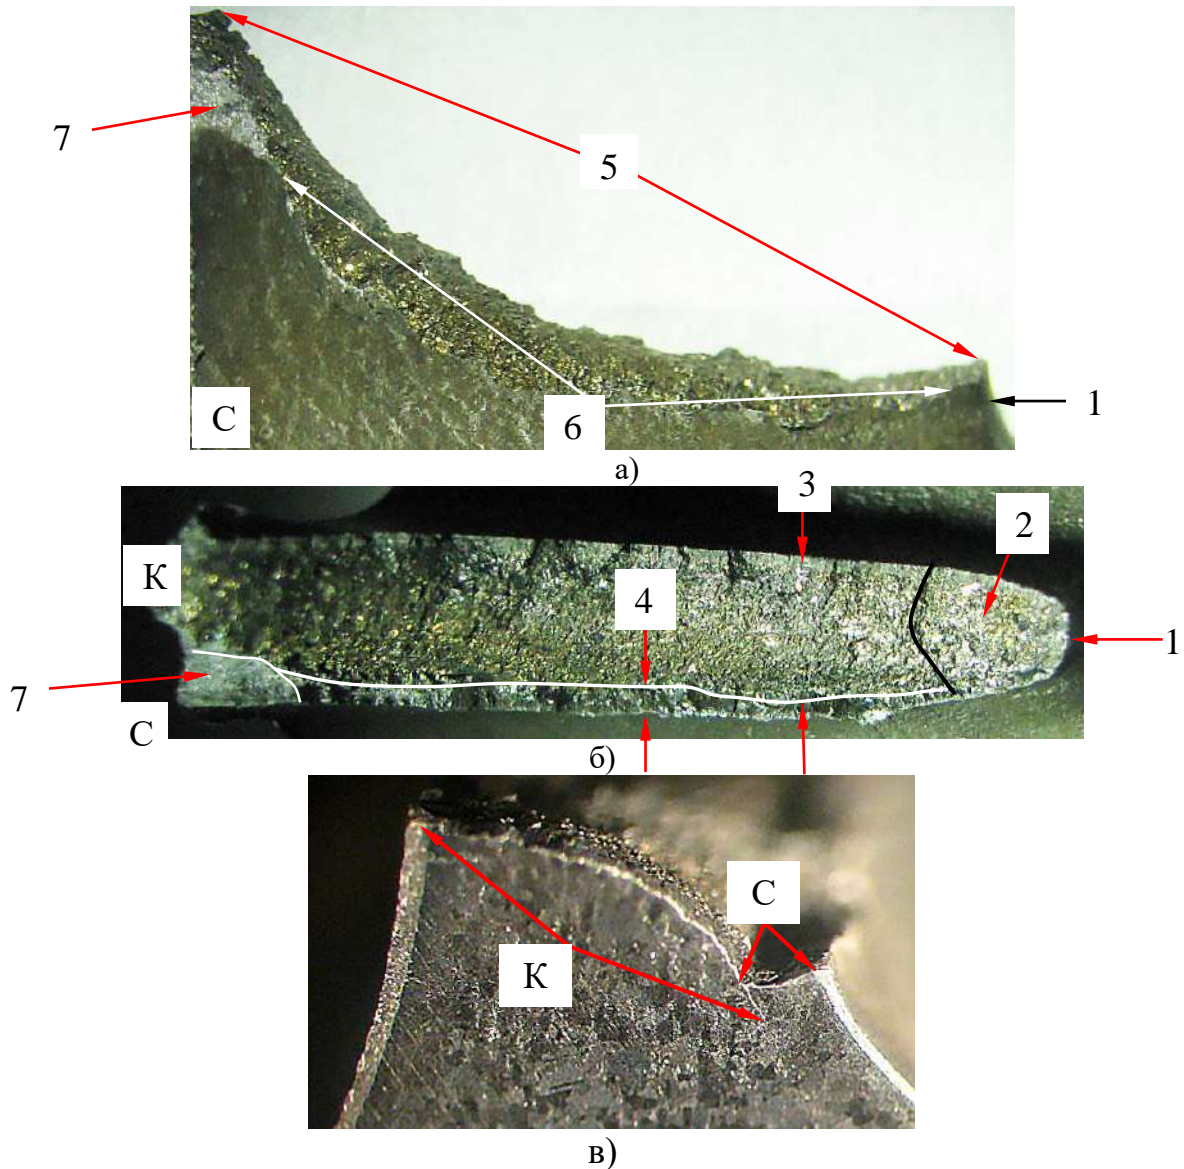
3 Макроизображение профиля трещины (а), поверхности излома (б) и поперечного сечения излома усталостной трещины (в) в выходной кромке лопатки СА. Стрелками показаны: 1 – выходная кромка лопатки, 2 – площадка отрыва, 3 – ширина трещины со стороны корытца, 4 – ширина трещины со стороны спинки, 5 – длина трещины со стороны корытца, 6 – длина трещины со стороны спинки, 7 – силовой долом. Увеличено.
